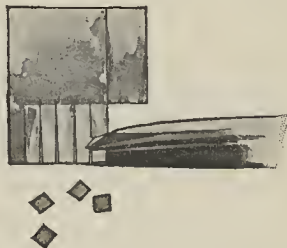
Manière de découper les paillons de soudure.
